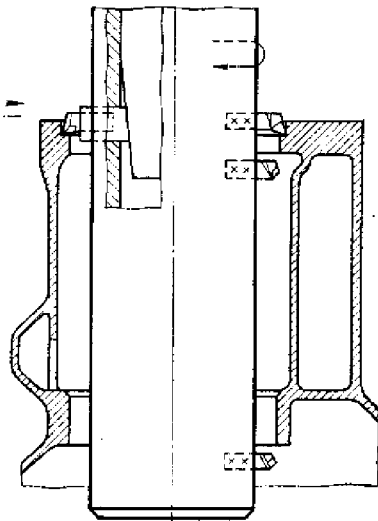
Схема обробки посадкових поверхонь у блоці під гільзу (суцільні стрілки - напрямок робочого руху; штрихові стрілки - напрямок зворотного руху)
